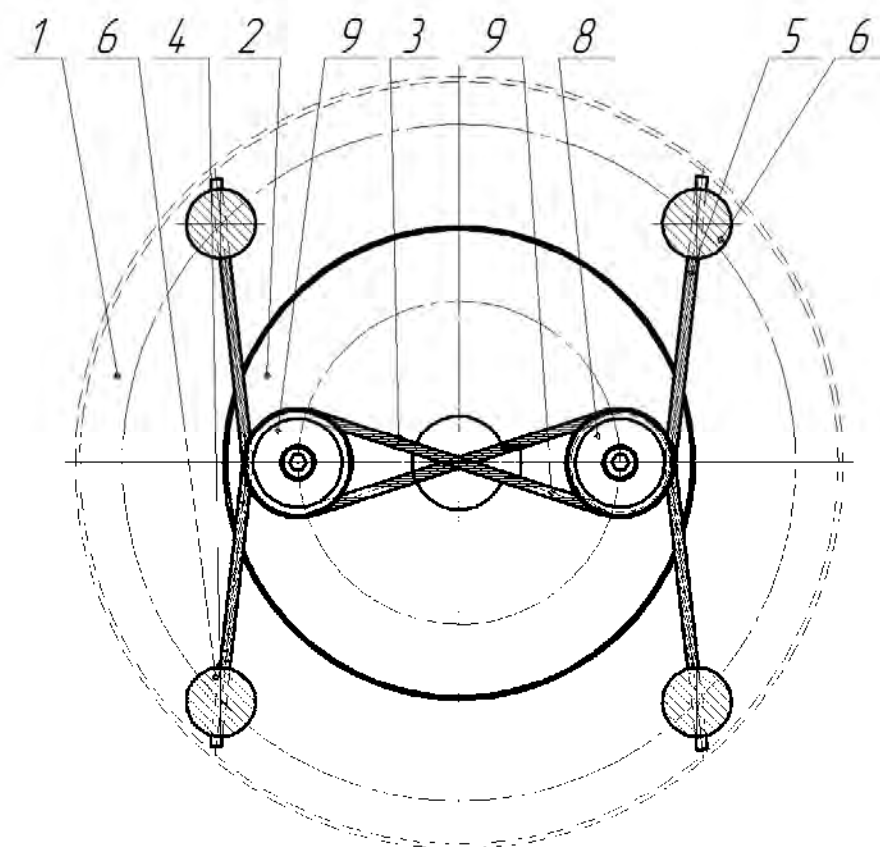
Загальний вид реверсивної канатно-роликової муфти
